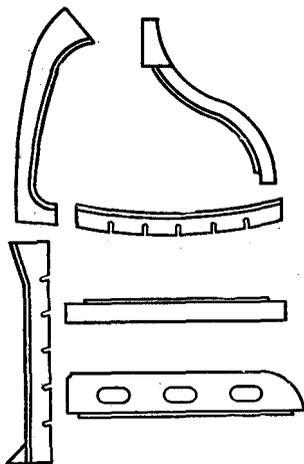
Типы составных сварных балок корпуса
